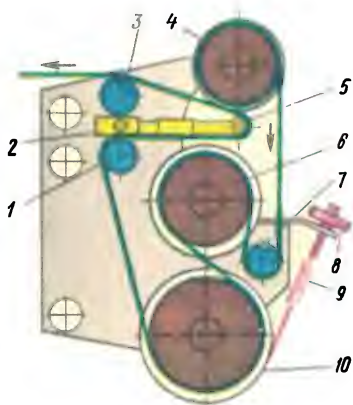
Кинематическая схема каретки бандажировочного станка с механизмом натяжения
